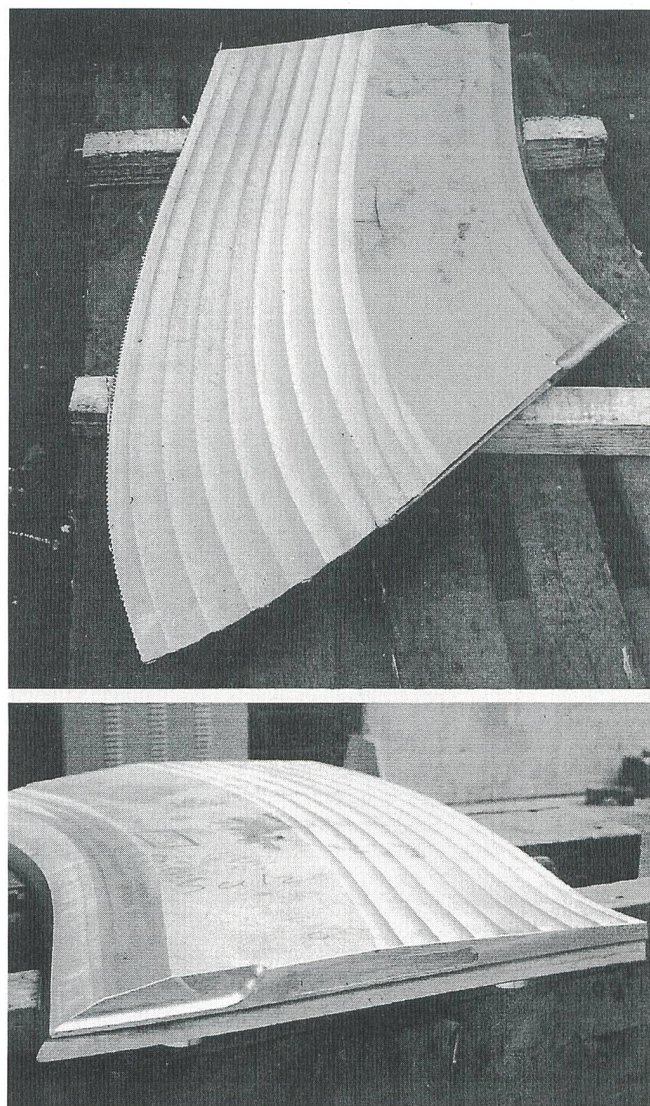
Gefrästes Schaukelblech vor dem Pressen
